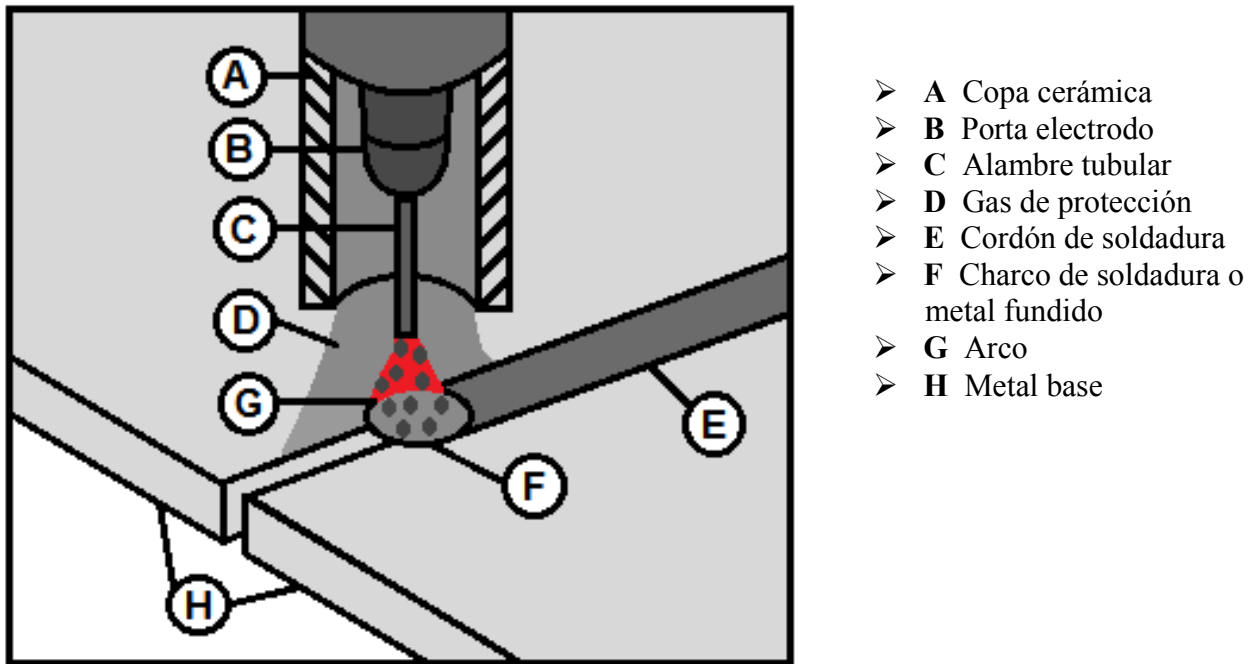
Esquema del proceso de soldadura por arco eléctrico con varilla tubular y gas de protección (8, 18)
